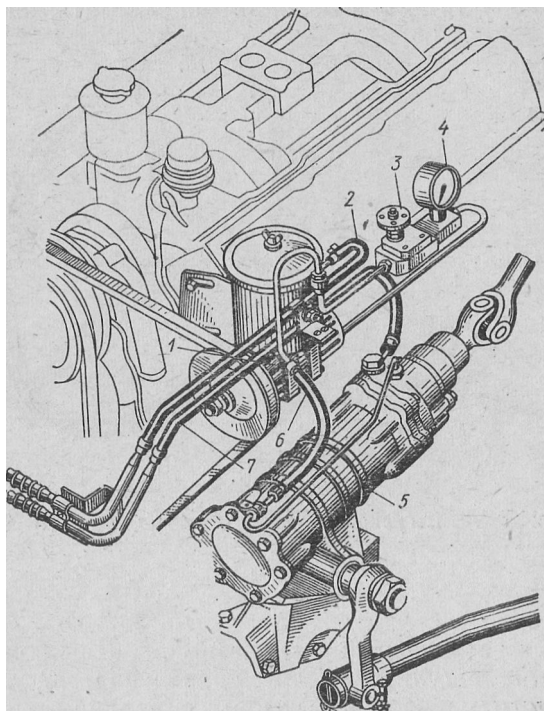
Схема проверки давления, развиваемого насосом гидроусилителя рулевого управления:
